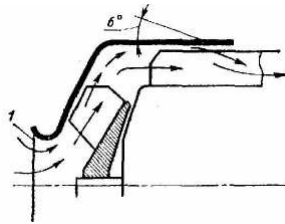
Конструкция вентиляционного узла с диффузором 1 на входе и с поджатием потока воздуха на выходе
